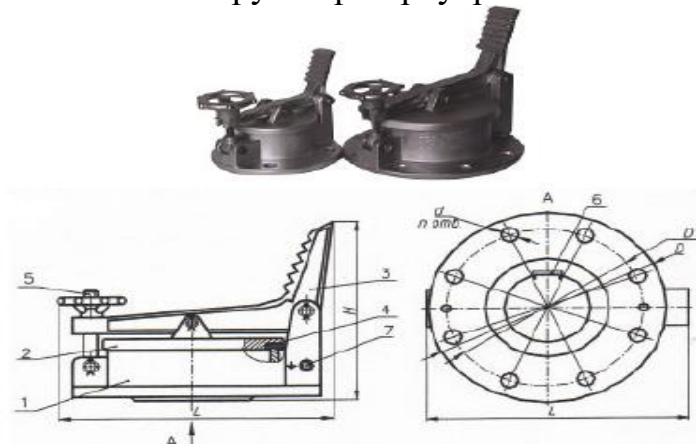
Люк замірний: 1 - корпус; 2 - кришка; 3 - педаль; 4 - гумова
